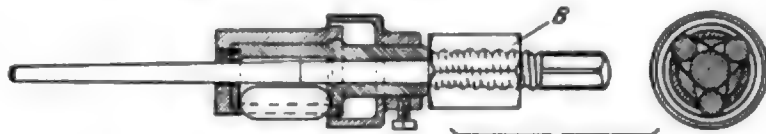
Werkzeug zum Aufwalzen der Heizrohre.
